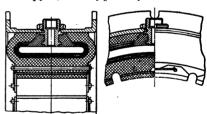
Баллон шиннопневматической муфты с внутренним расположением колодок
